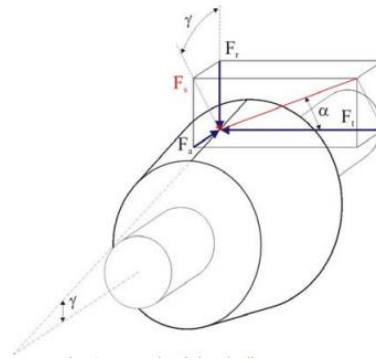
FUERZAS ACTUANTES ENGRANAJE CÓNICO DE DIENTES RECTOS
